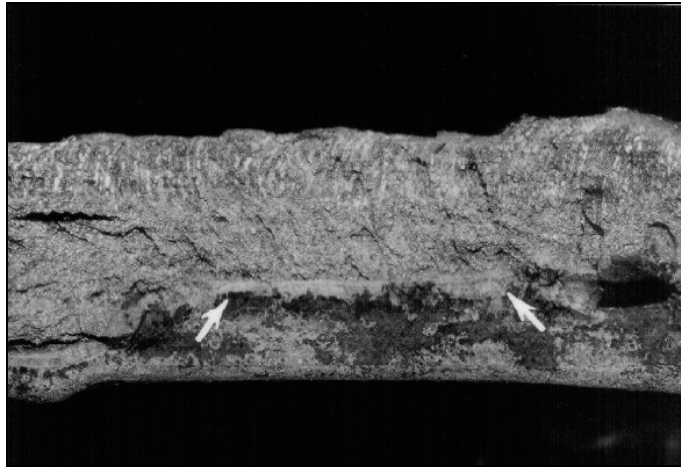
Fractura ocasionada por combinación de soldadura defectuosa y fatiga
